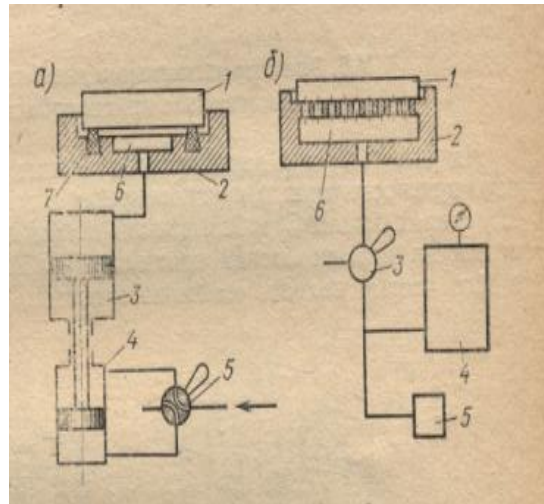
Схема пристосувань з вакуумним приводом:
